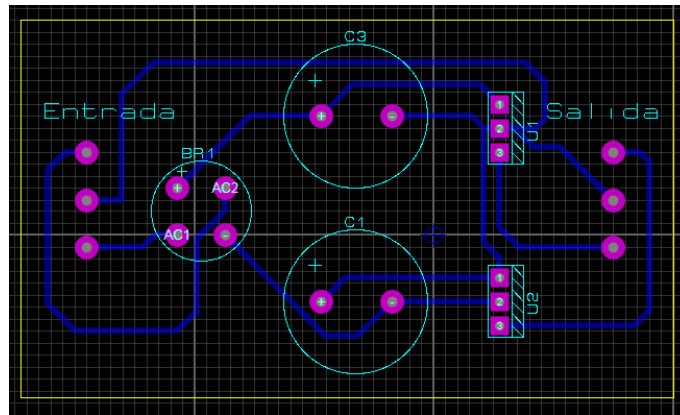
Diseño del PCB para la fuente de voltaje simétrica de 24 volts.
